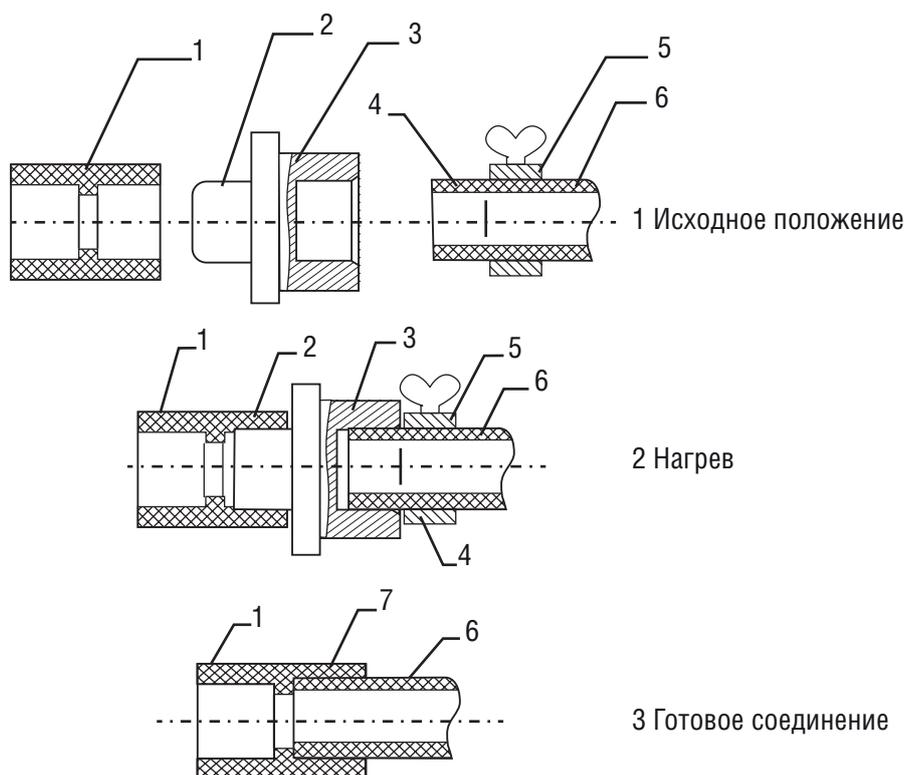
Последовательность процесса сварки в раструб напорной трубы и соединительной детали из полипропилена рандомсополимера.
